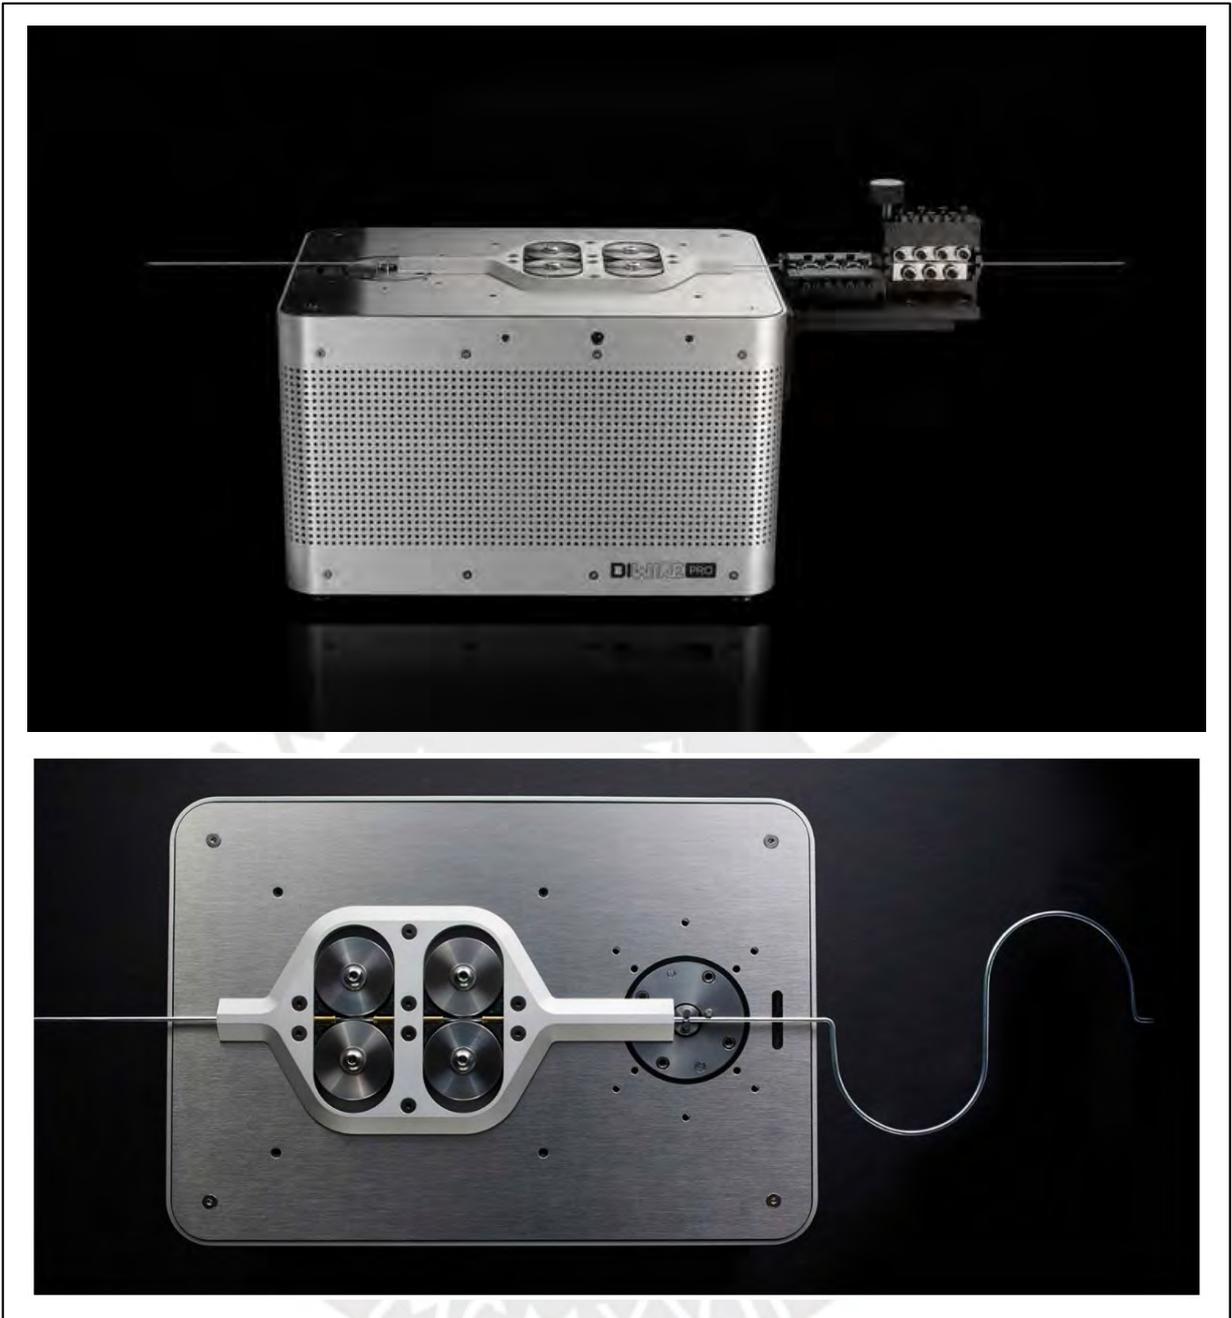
Dobladora de varilla CNC DIWIRE PRO.
